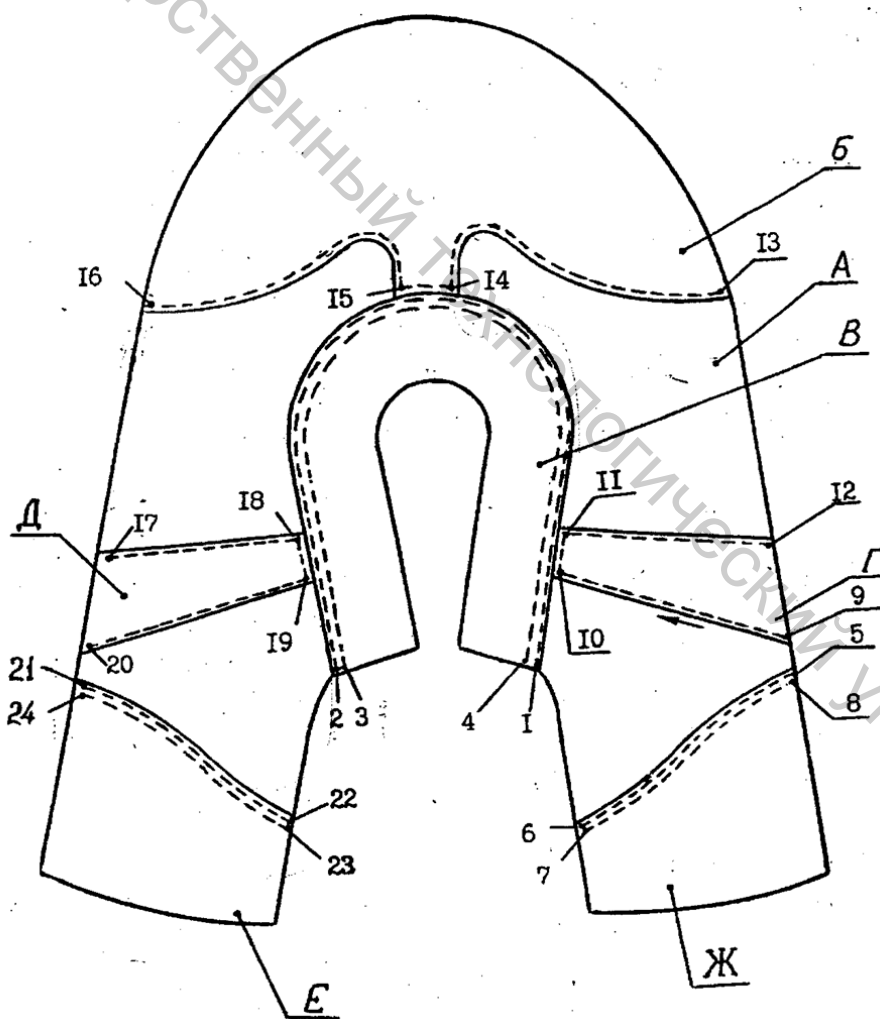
Заготовка верха обуви с контурами соединительных швов
